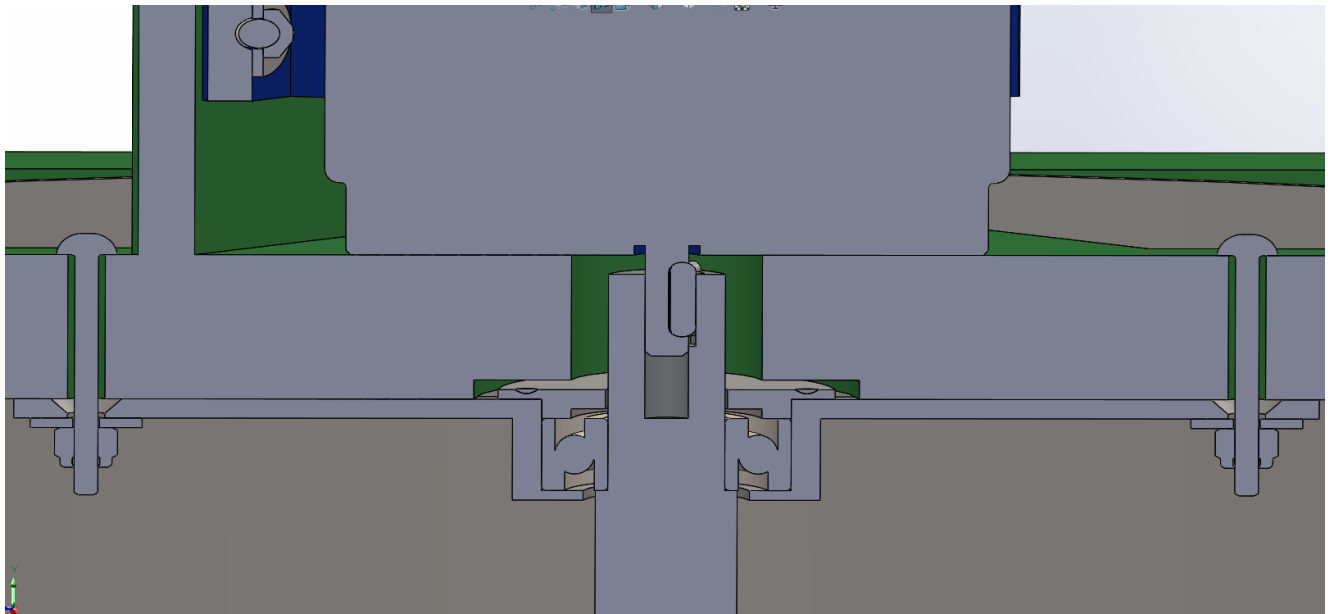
Зовнішній вигляд шпонкового з'єднання вала двигуна зі шнеком.
